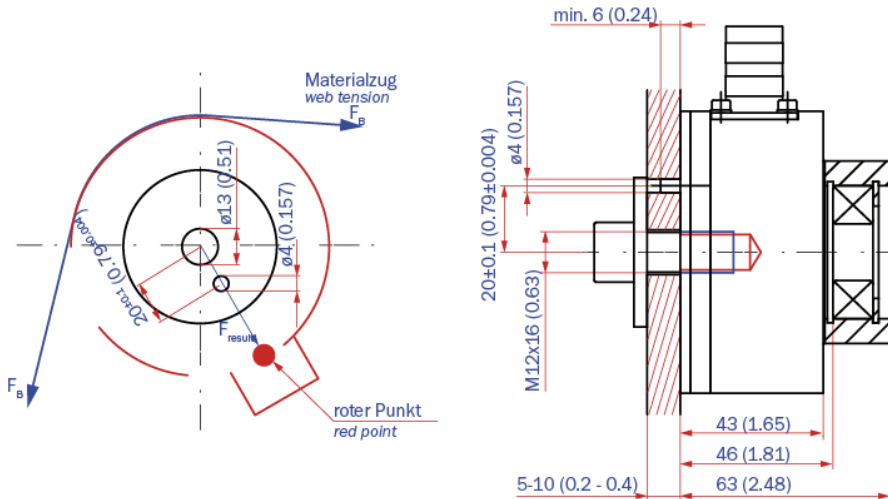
Abmessungen am Maschinenrahmen für FL Montage
